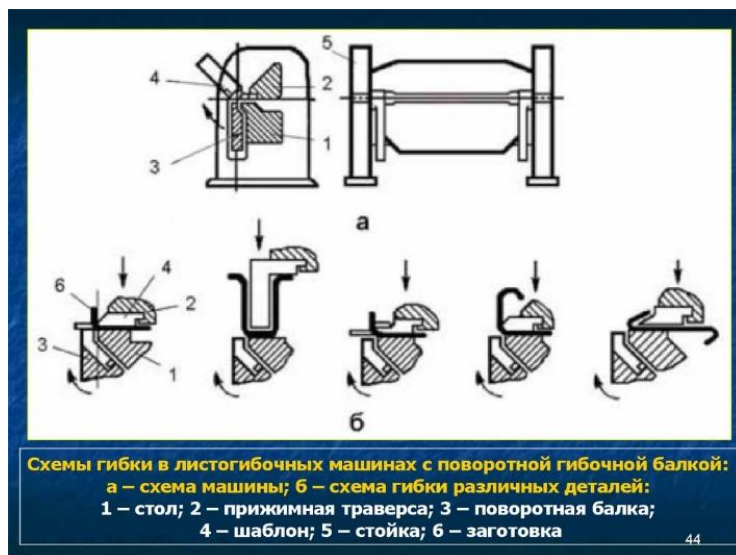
Схема гнуща заготовки поворотною балкою
